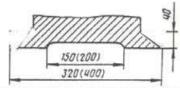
Посадочные и присоединительные размеры направляющих станины (в скобках даны размеры для станка 6Т83Ш)
